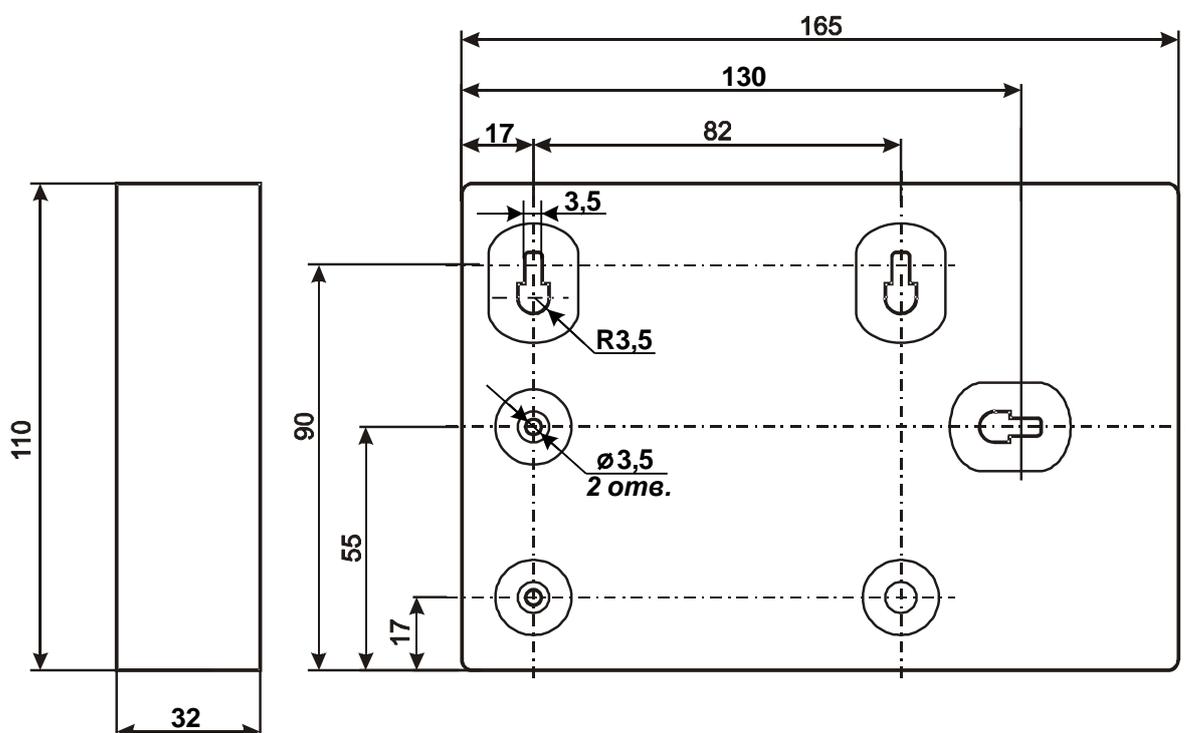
Габаритные и присоединительные размеры (исп. IP20)
